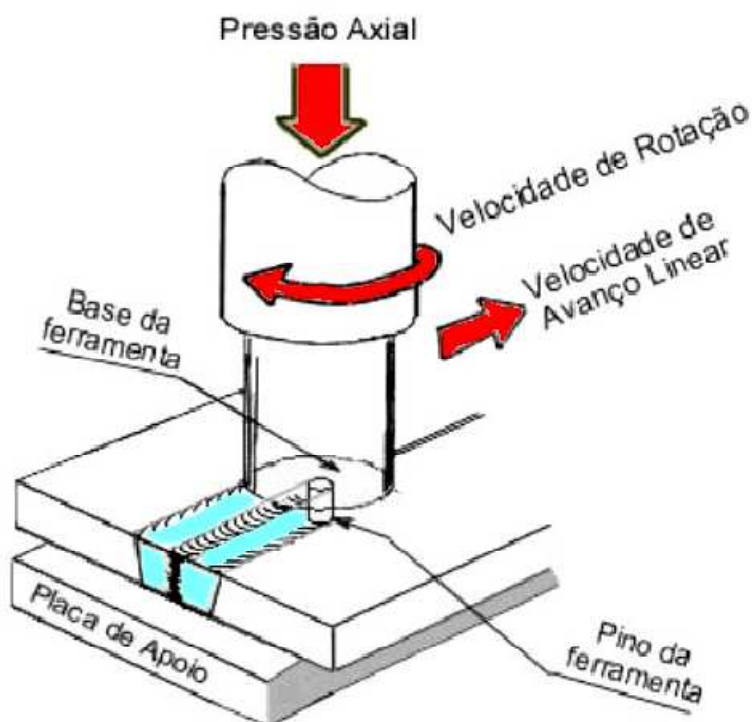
Modo de Funcionamento de Soldadura por Fricção Linear [22]
